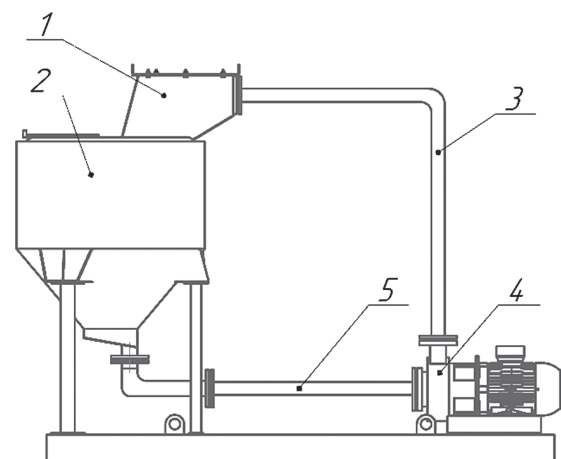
Конструктивно-технологическая схема установки для приготовления жидких сахаристых кормов:
